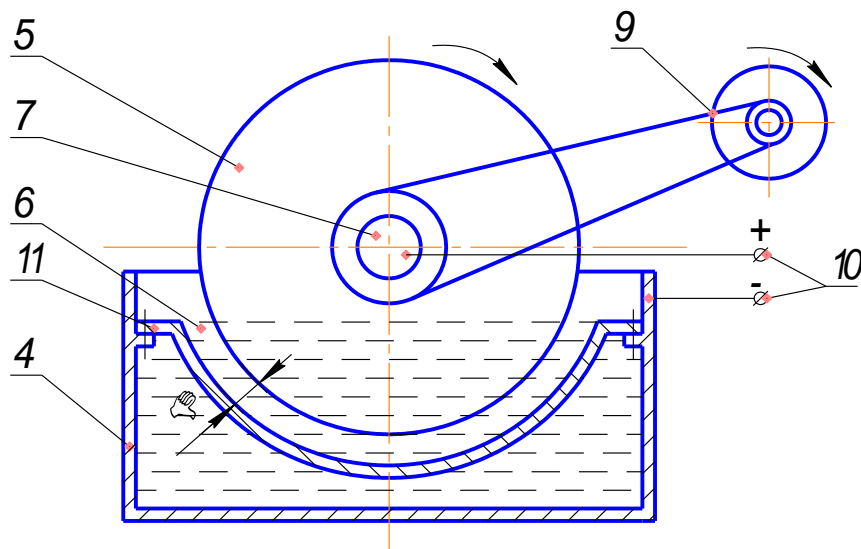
Вид збоку (в розрізі) пристрою для проведення електрохімічної обробки пошкодженої поверхні осердя короткозамкненого ротора
